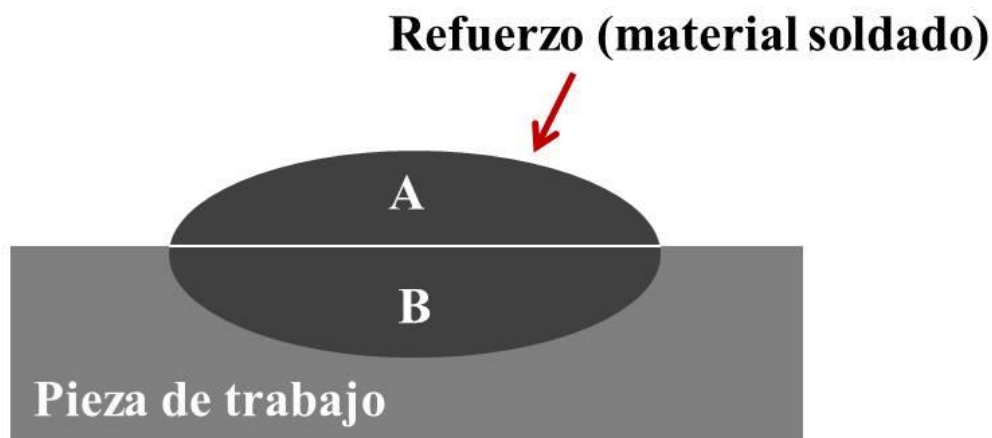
Esquema de área transversal con partes de una soldadura de recubrimiento, imagen adaptada de [22].
